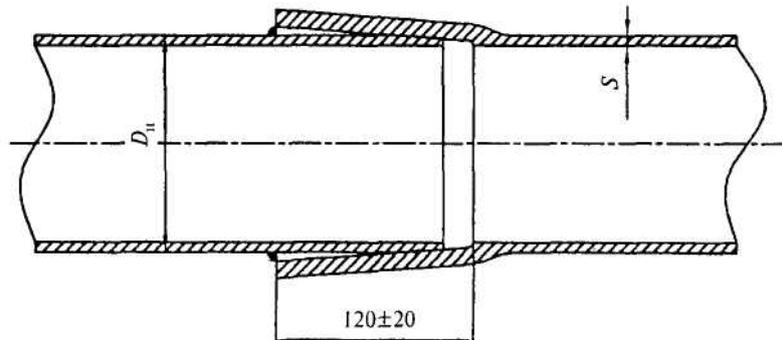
Схема сварного нахлестного соединения
